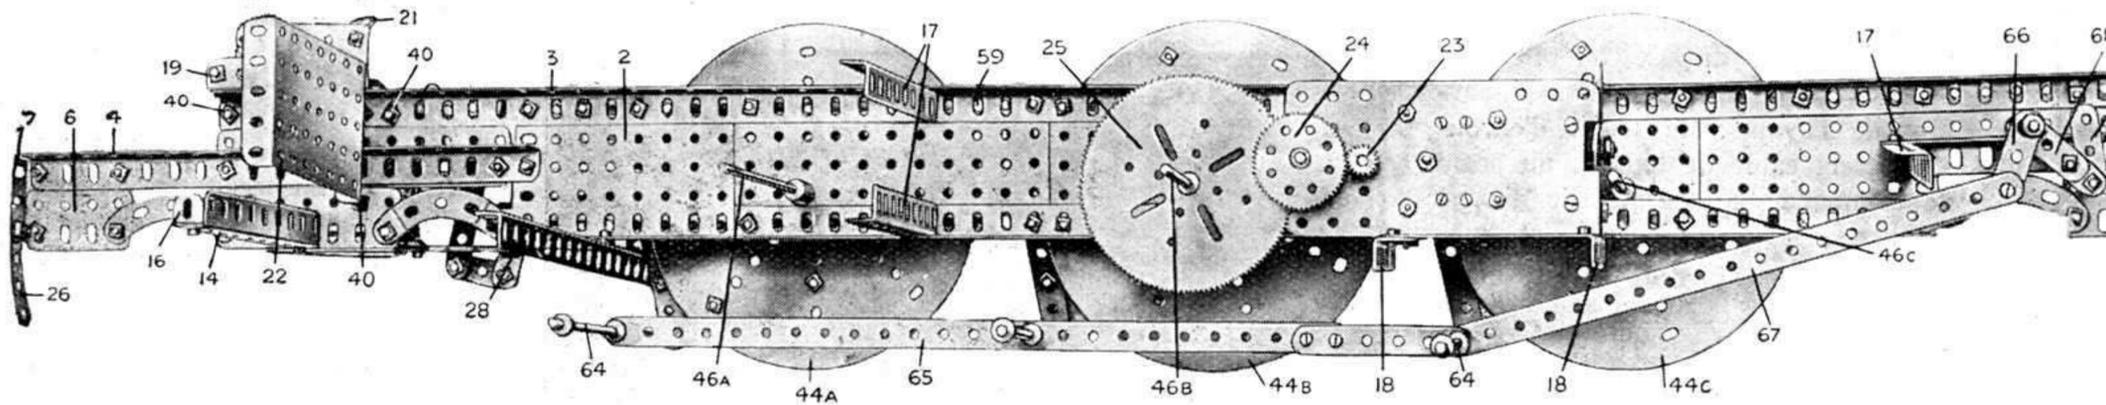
Vue intérieure du côté droit du châssis montrant la position du Moteur et des Engrenages démultiplicateurs.
